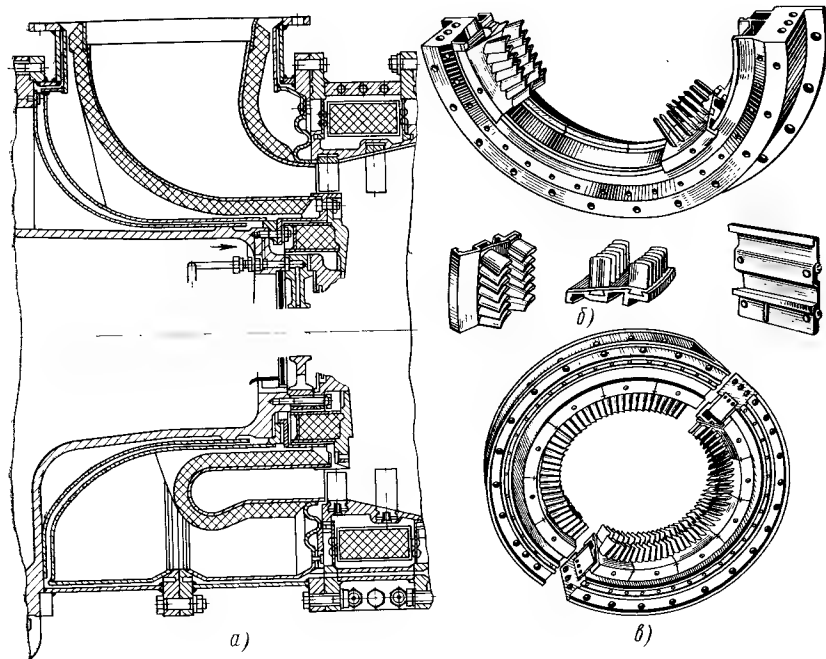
Корпус турбины высокого давления ГТУ ТА фирмы Рустон
